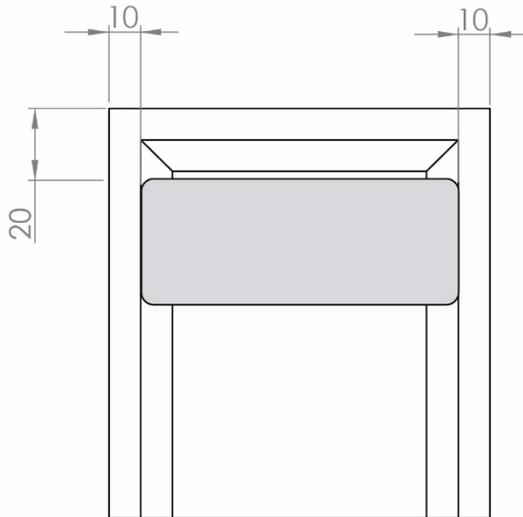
Pote CANNACREM: Etiquetado/Rotulado
